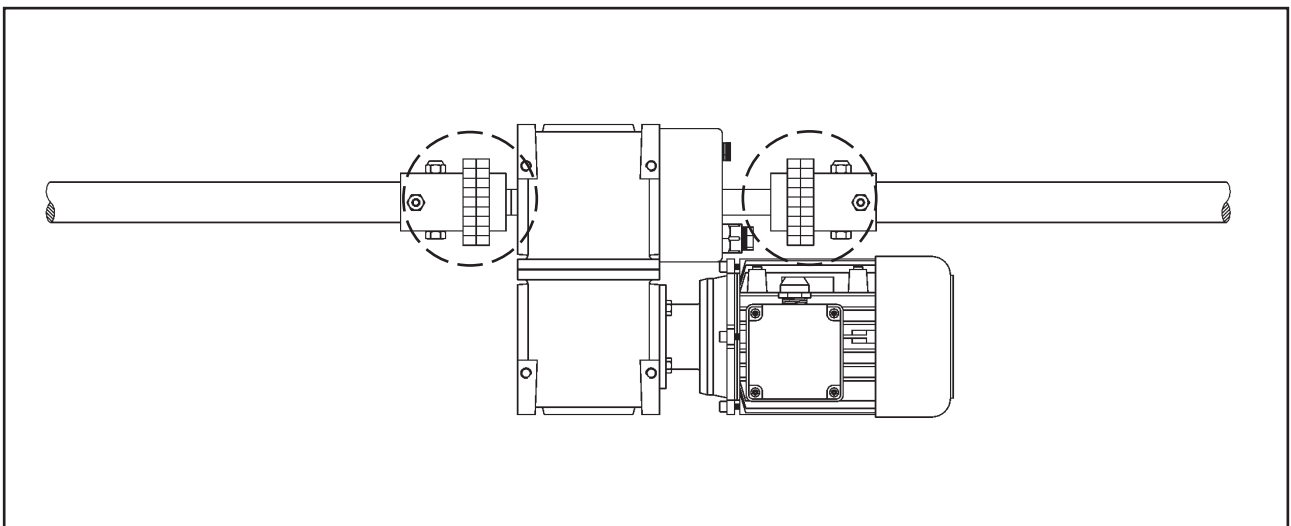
Gearmotor monteret med kædekoblinger.
